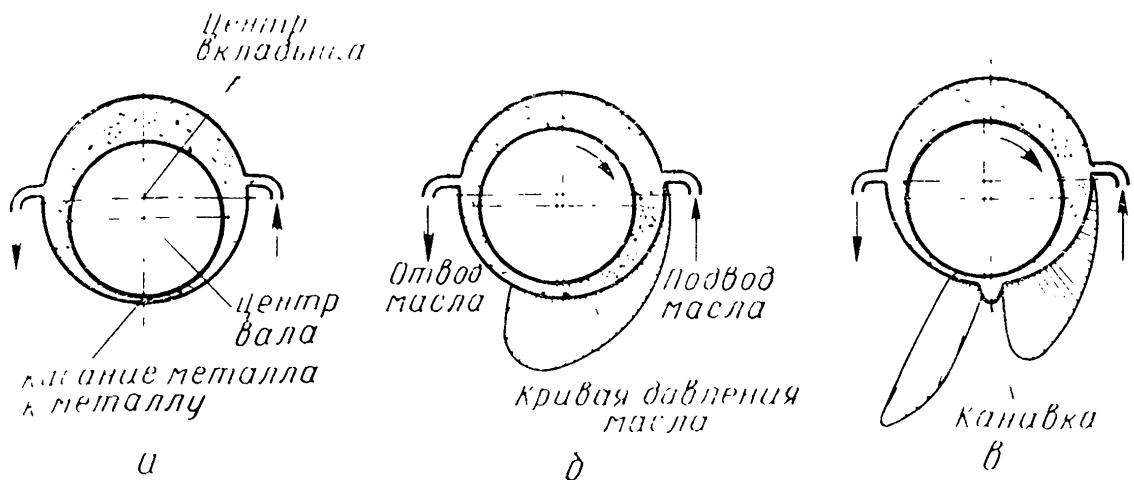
Смазка опорного подшипника (зазор между шейкой вала и подшипником для наглядности значительно увеличен):
